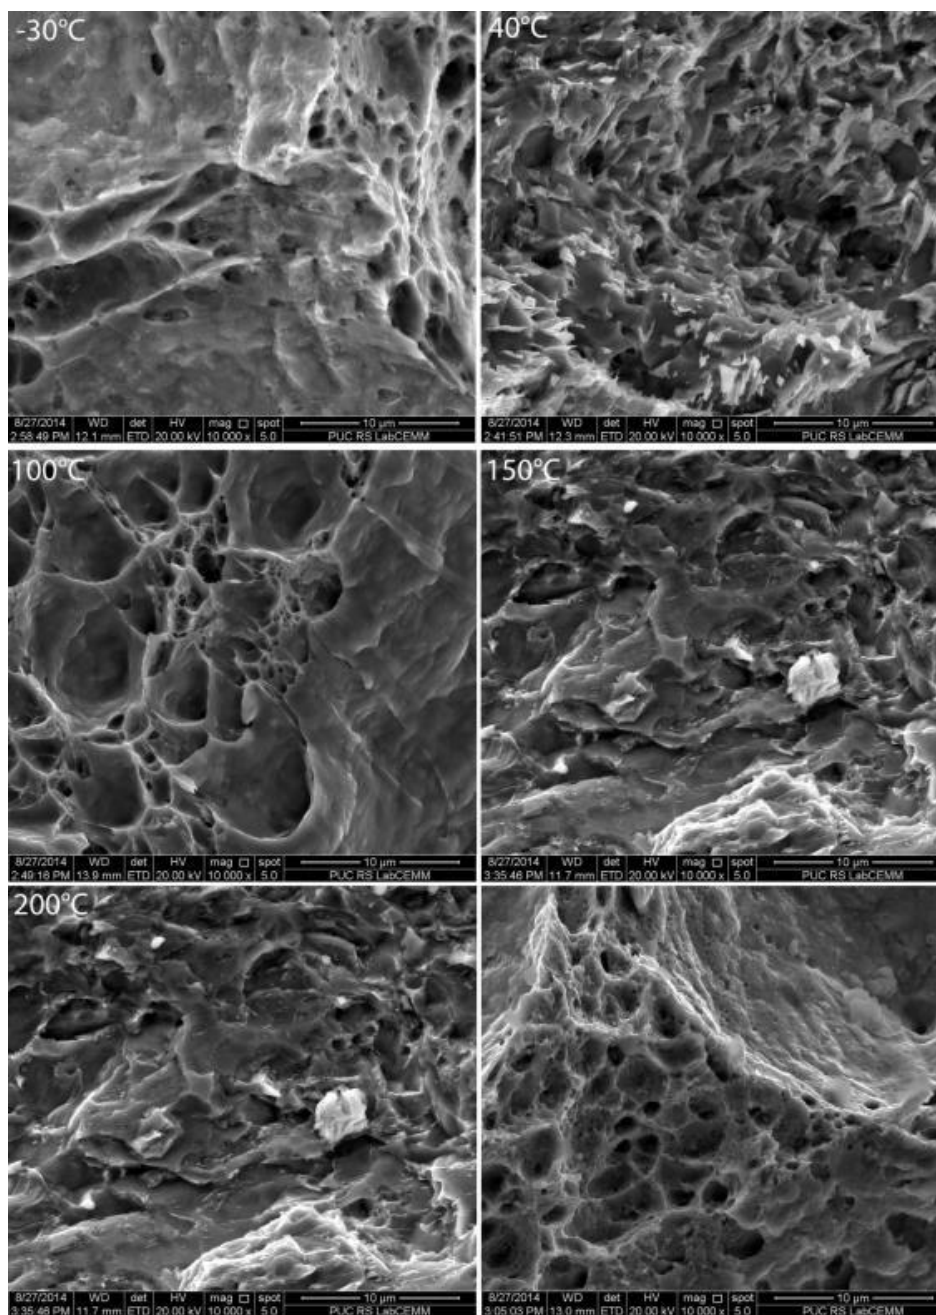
Imagens do MEV das superfícies de fratura das amostras após o ensaio de Impacto Charpy-V realizada a 0 °C. O número posicionado no canto superior esquerdo de cada amostra indica a temperatura de pré-aquecimento da soldagem e MB é metal base.
